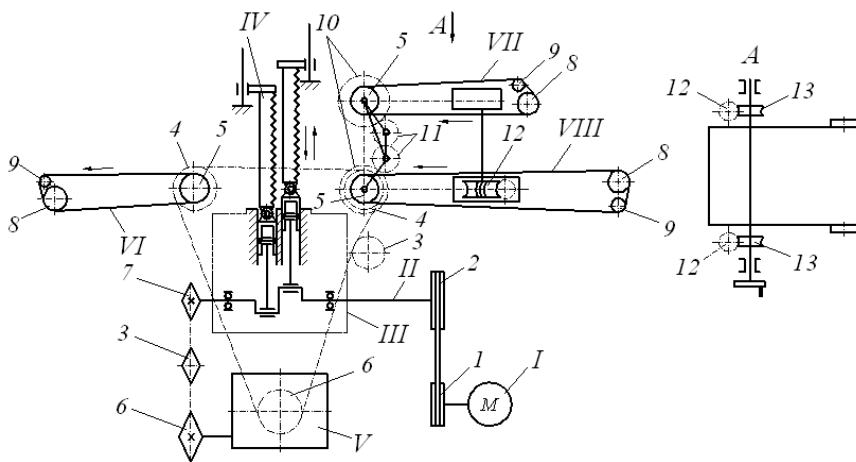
Схема приводу механізмів хліборізальної машини А-2ХРЗ-П: I – електродвигун; II – колінчастий вал коробки привідної; III – коробка привідна; IV – касета з ножовою рамою; V – редуктор; VI – конвеєр видачі; VII – конвеєр верхній; VIII – конвеєр подачі; 1, 2 – шківів; 3, 4, 6, 7 – зірочки; 5 – барабан приводний; 8 – самоцентрувальний натяжний барабан; 9 – відхиляючий ролик; 10 – 13 – зубчаті колеса
